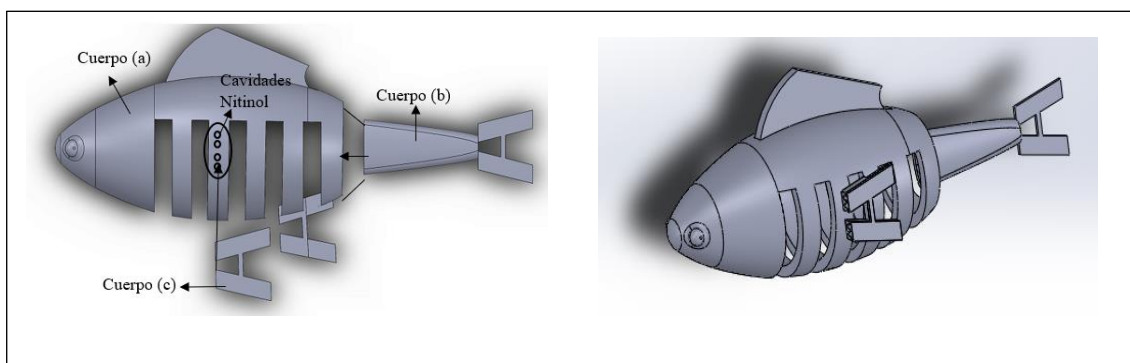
Diseño del prototipo ensamblado en SolidWorks
